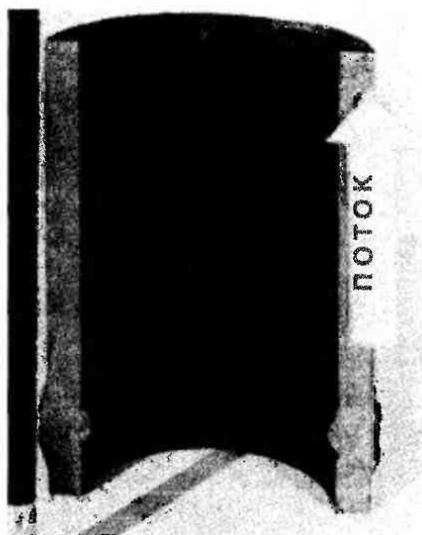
Типичное разрушение, вызванное химической коррозией (углубляющиеся канавки), после сварного шва с опорным кольцом.
